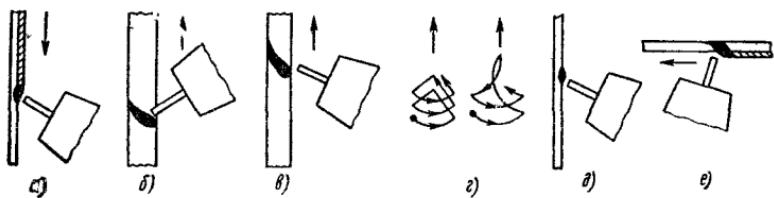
Схемы расположения электрода и поперечных колебаний электрода при сварке в CO_2 швов:
